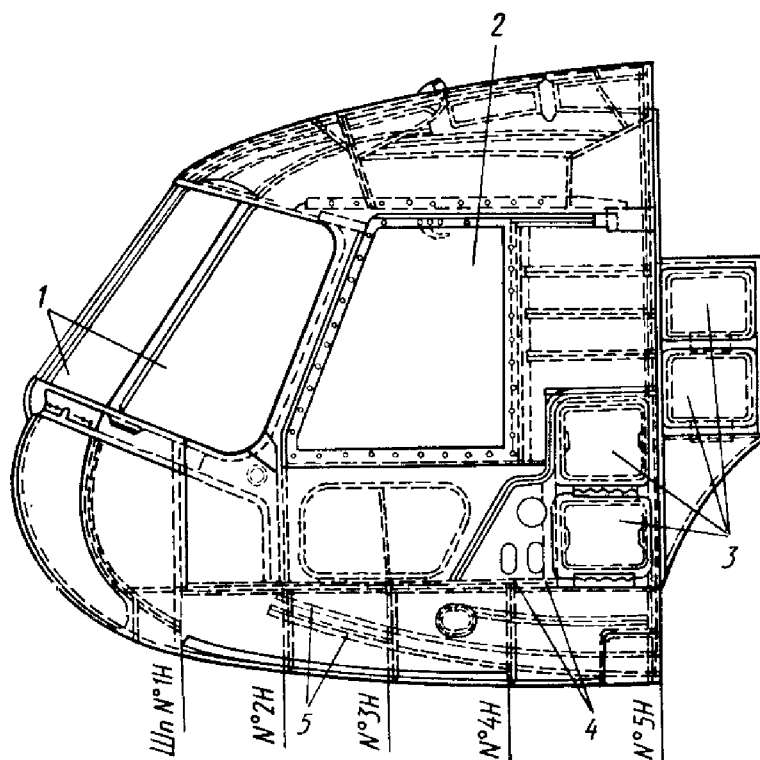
Носовая часть фюзеляжа балочного типа вертолета Ми-8 [2]:
